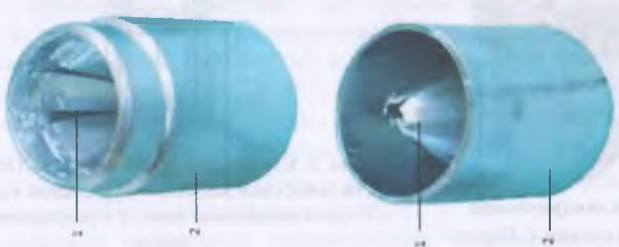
Усовершенствованный пружинистый кернодержатель:
